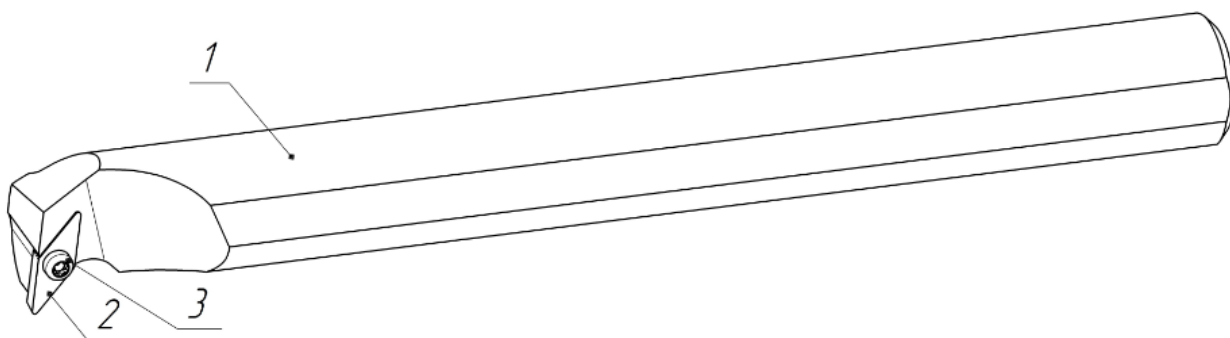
Розточувальний різець A32T-SVUBR 16 [1]
